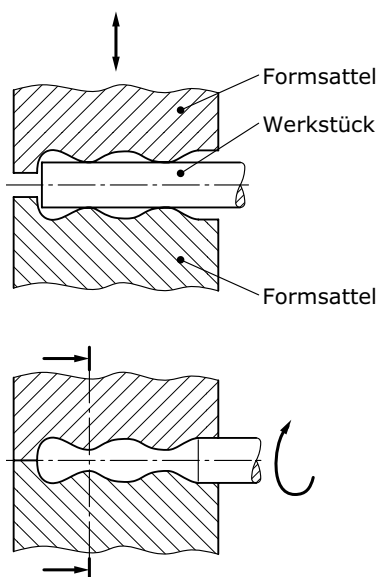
mfZ) Prinzip des Gesenkformens, hier mit einer Stufe
